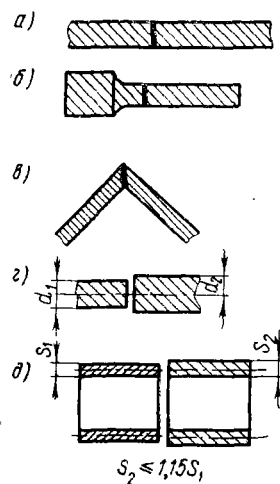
Соединения при стыковой контактной сварке:
